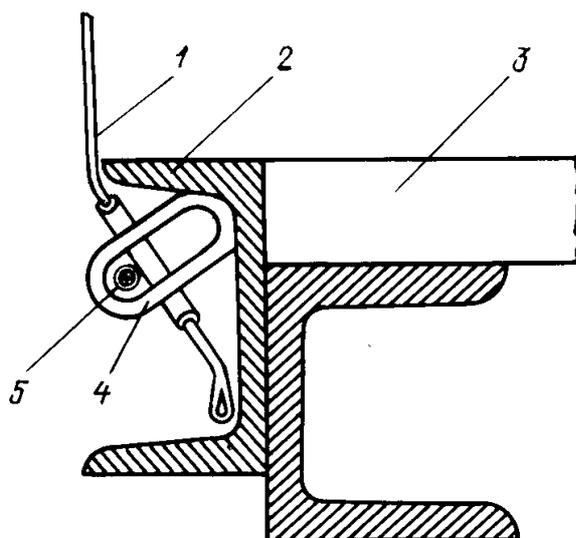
Устройство для крепления чехла к контейнеру:
